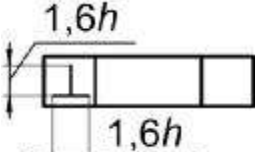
Обозначение допусков формы и расположения поверхностей
